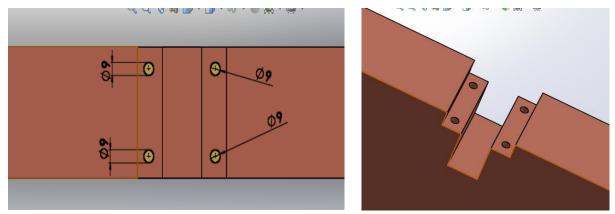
Barrenos para la colocación de tornillos en la barra paralela.
